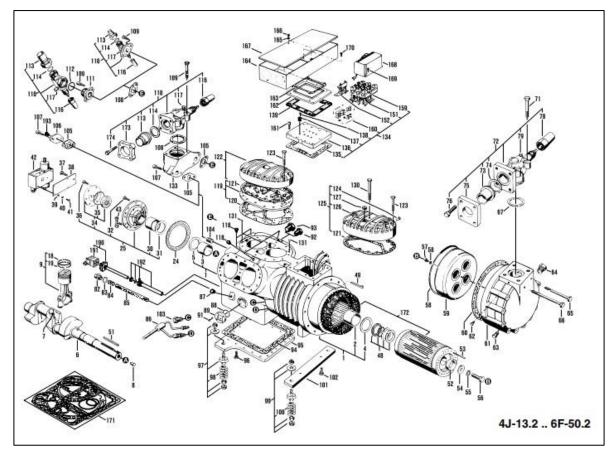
Despiece de Bitzer típico BE6 Fuente: (Bitzer)
